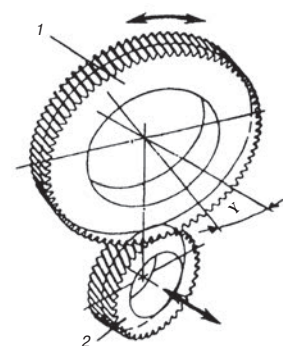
Схема обработки заготовки хонем с внешним зацеплением.
